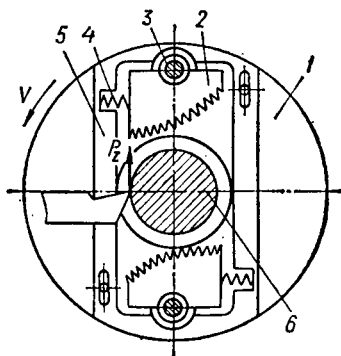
Схема токарного подающего патрона с приводом от сил резания
